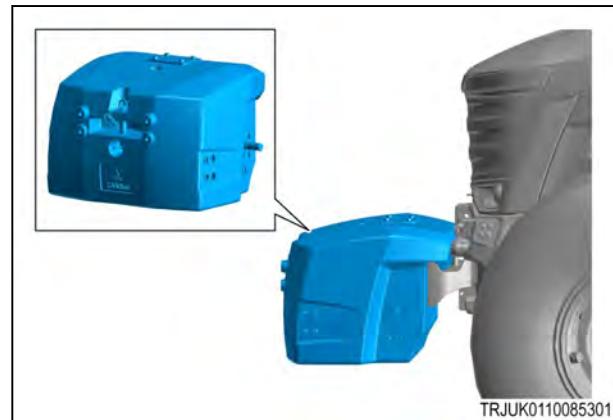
Contrapeso de una sola pieza en un soporte delantero
